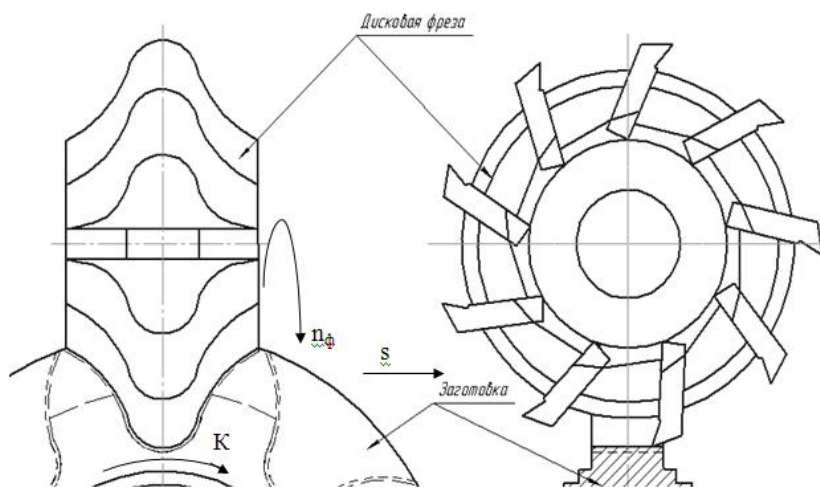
Фрагмент наладки горизонтально-фрезерной операции зубчатого венца колеса движителя БСП дисковой фасонной фрезой
